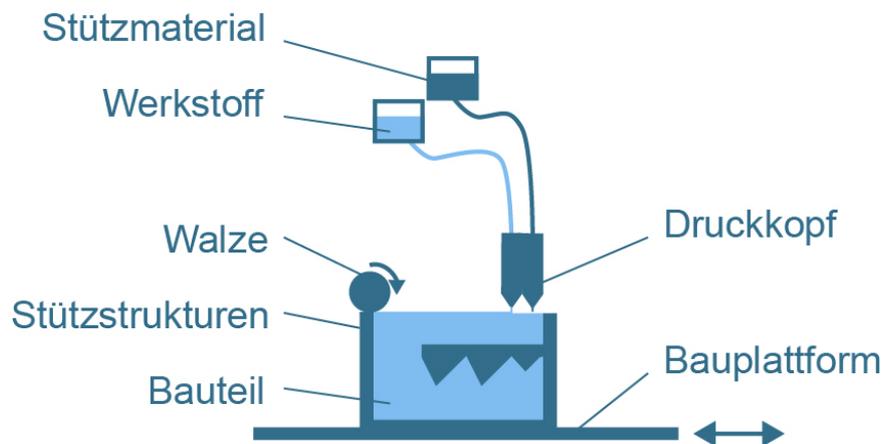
Aufbau und Elemente einer MJM-Anlage
